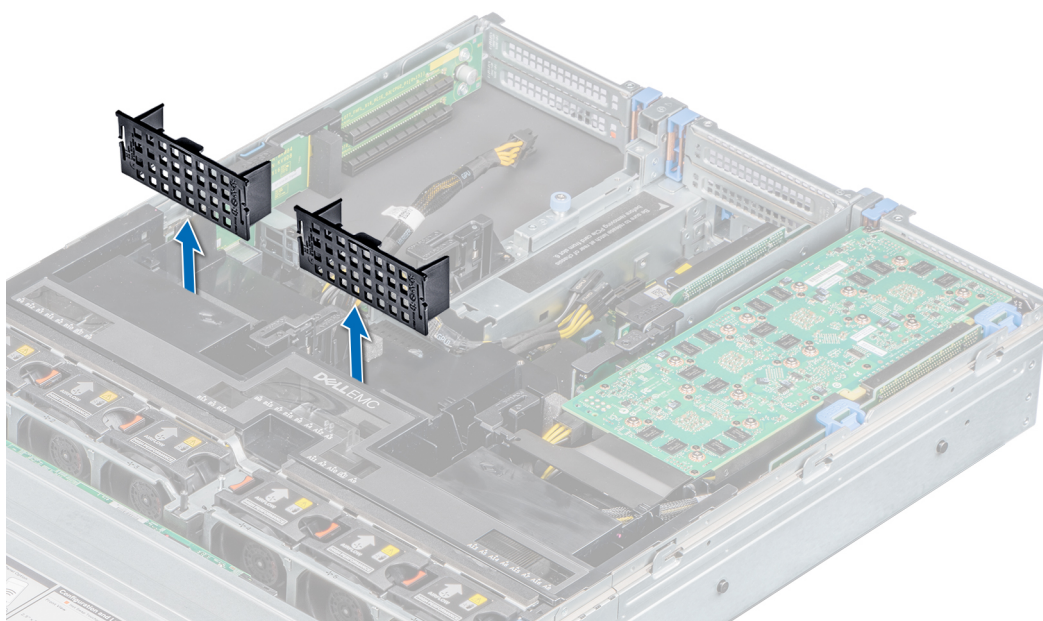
Extracción de la cubierta de relleno de las ranuras para cubierta para flujo de aire GPU
